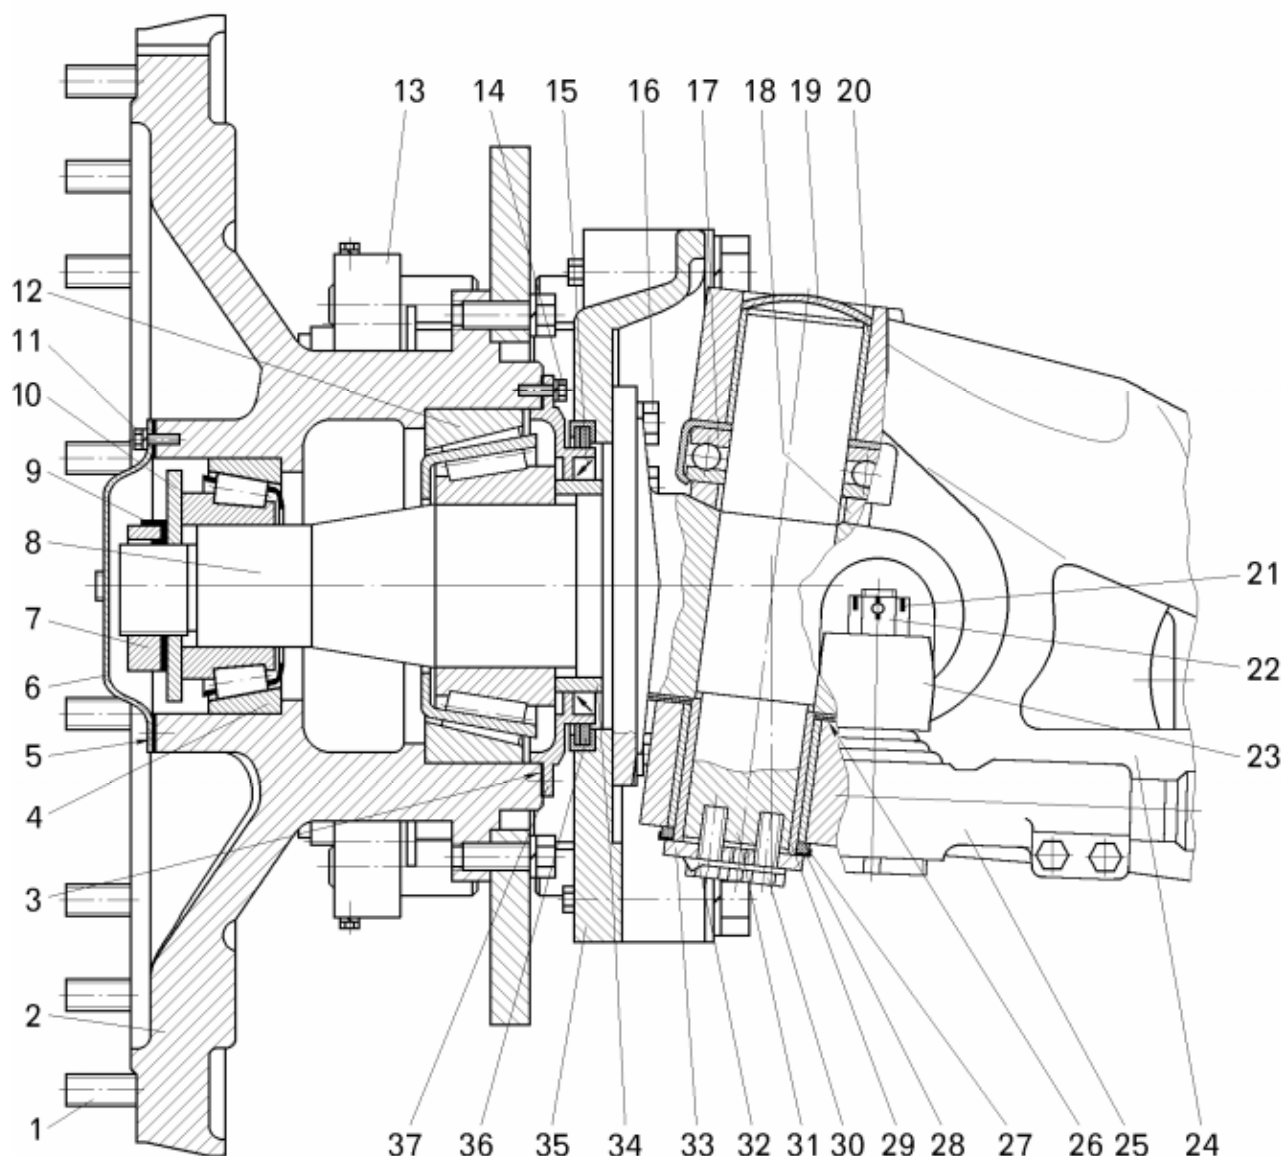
Передняя ось самосвала БелАЗ-75473 с гидравлическим приводом тормозных механизмов:
